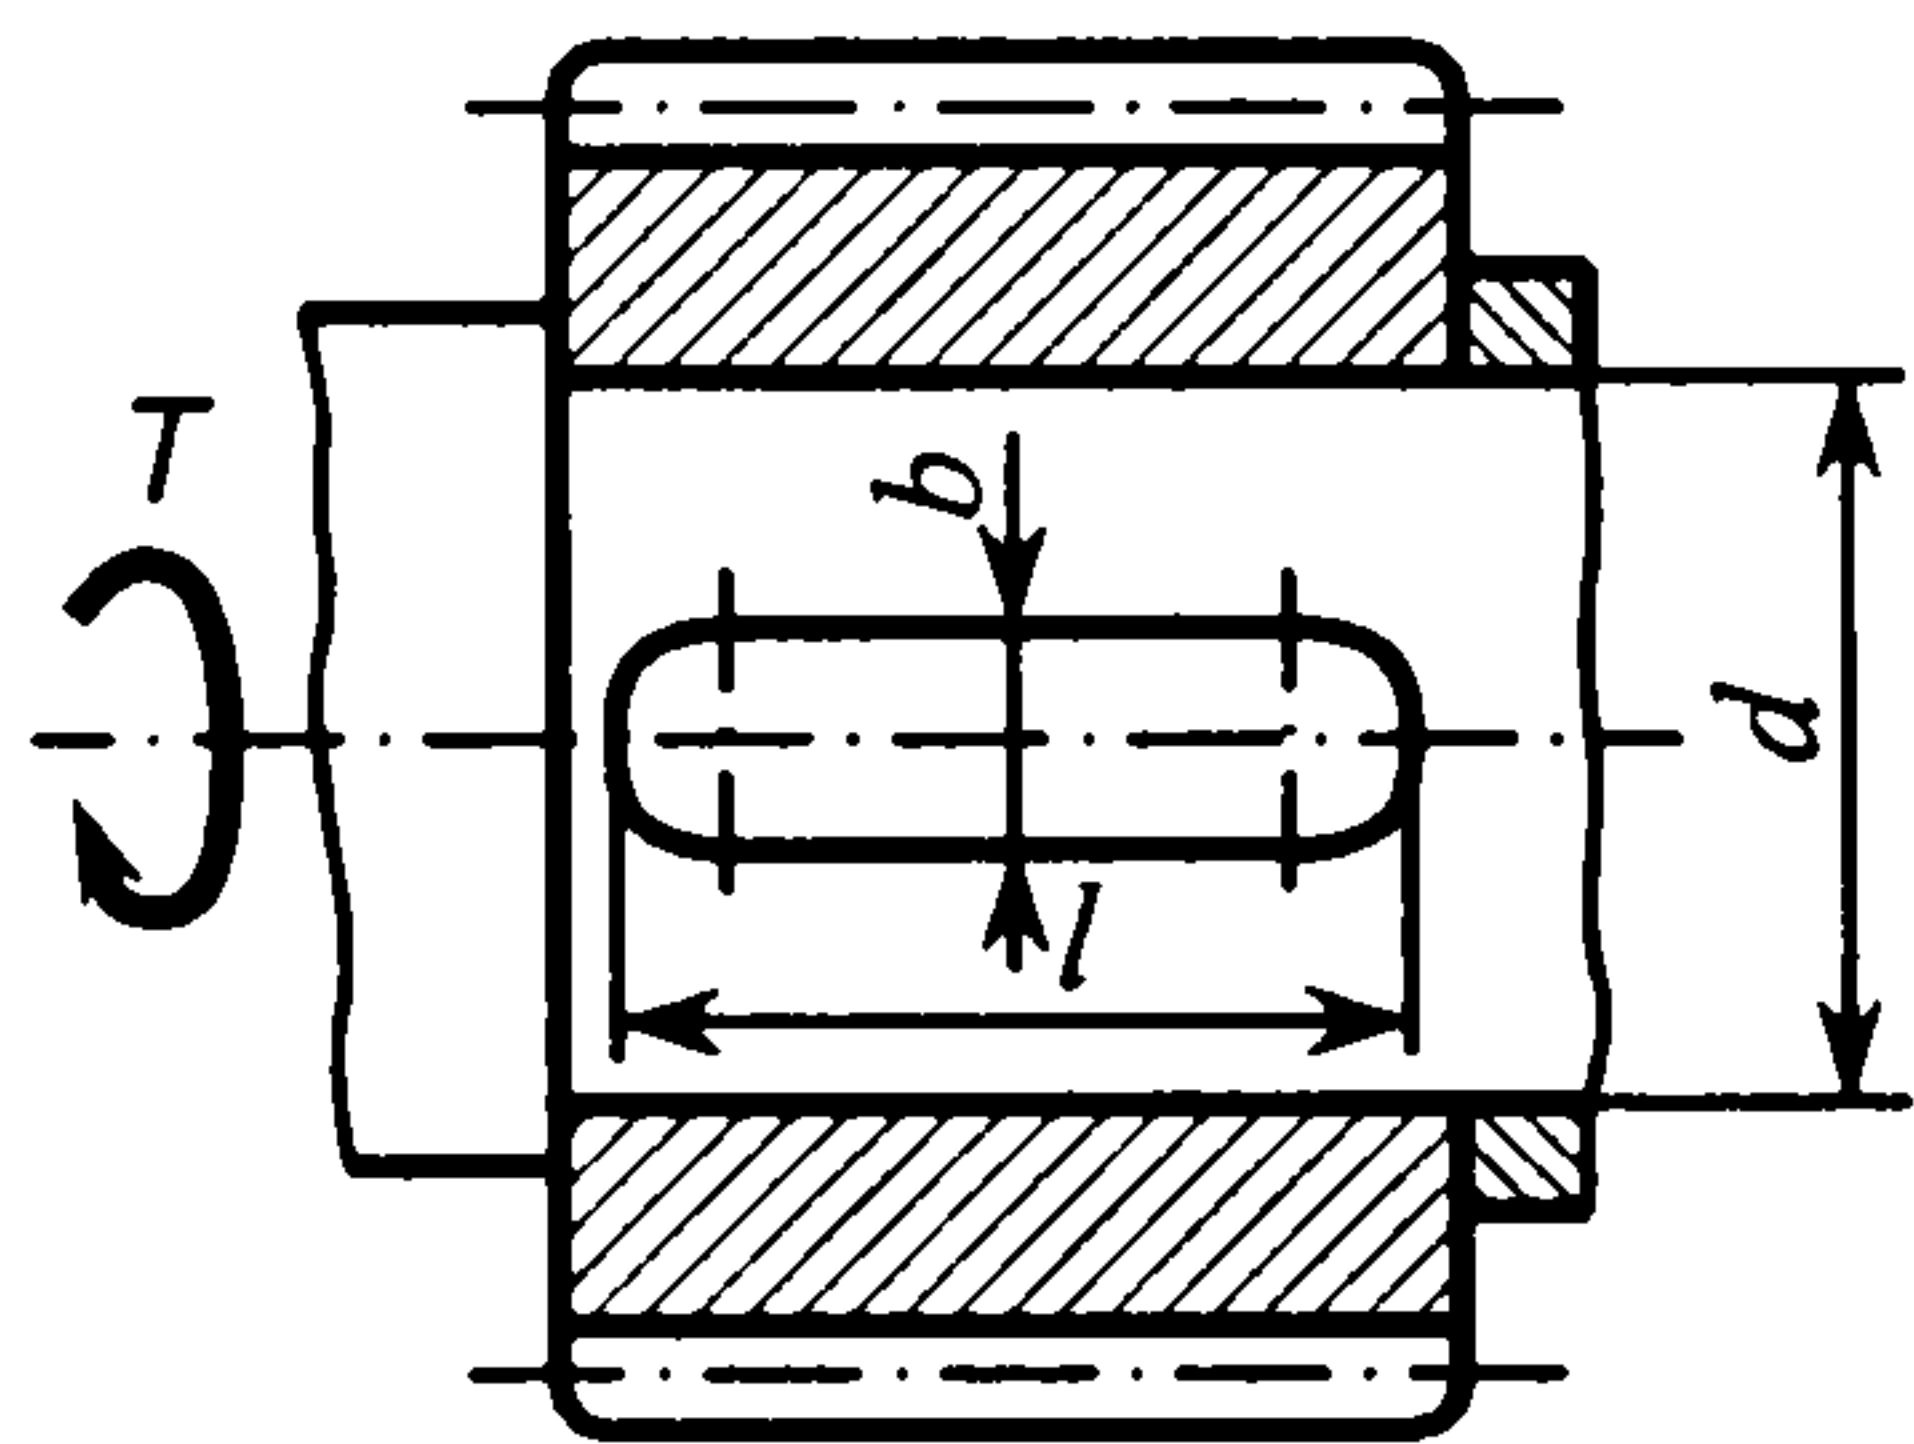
З'єднання вала із зубчастим колесом за допомогою призматичної шпонки
